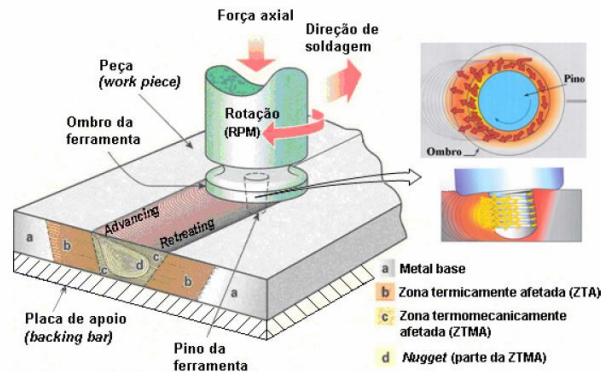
Processo de soldagem por FSW-Friction Stir Welding. (CRUZ, 2009).
